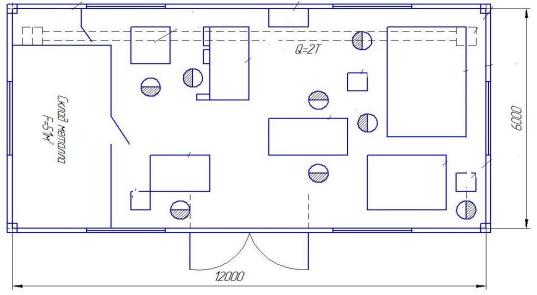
Сборочно-сварочных цех для изготовления опоры.
